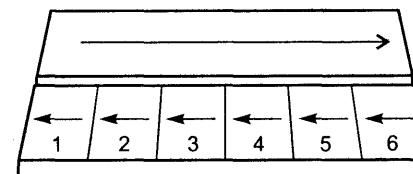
Сварка обратноступенчатым способом
